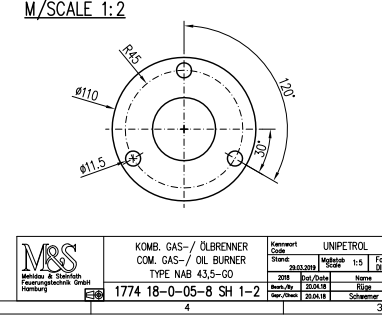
DETAIL "X": BEFESTIGUNG LUFTVORLAGE
